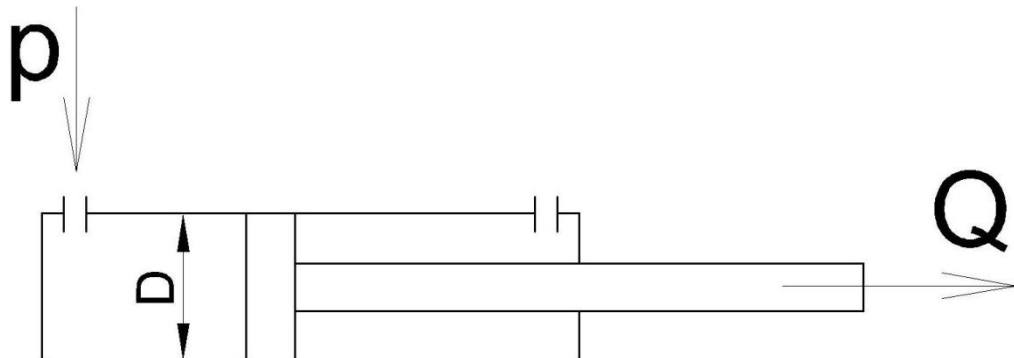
Розрахункова схема пневмоциліндра
